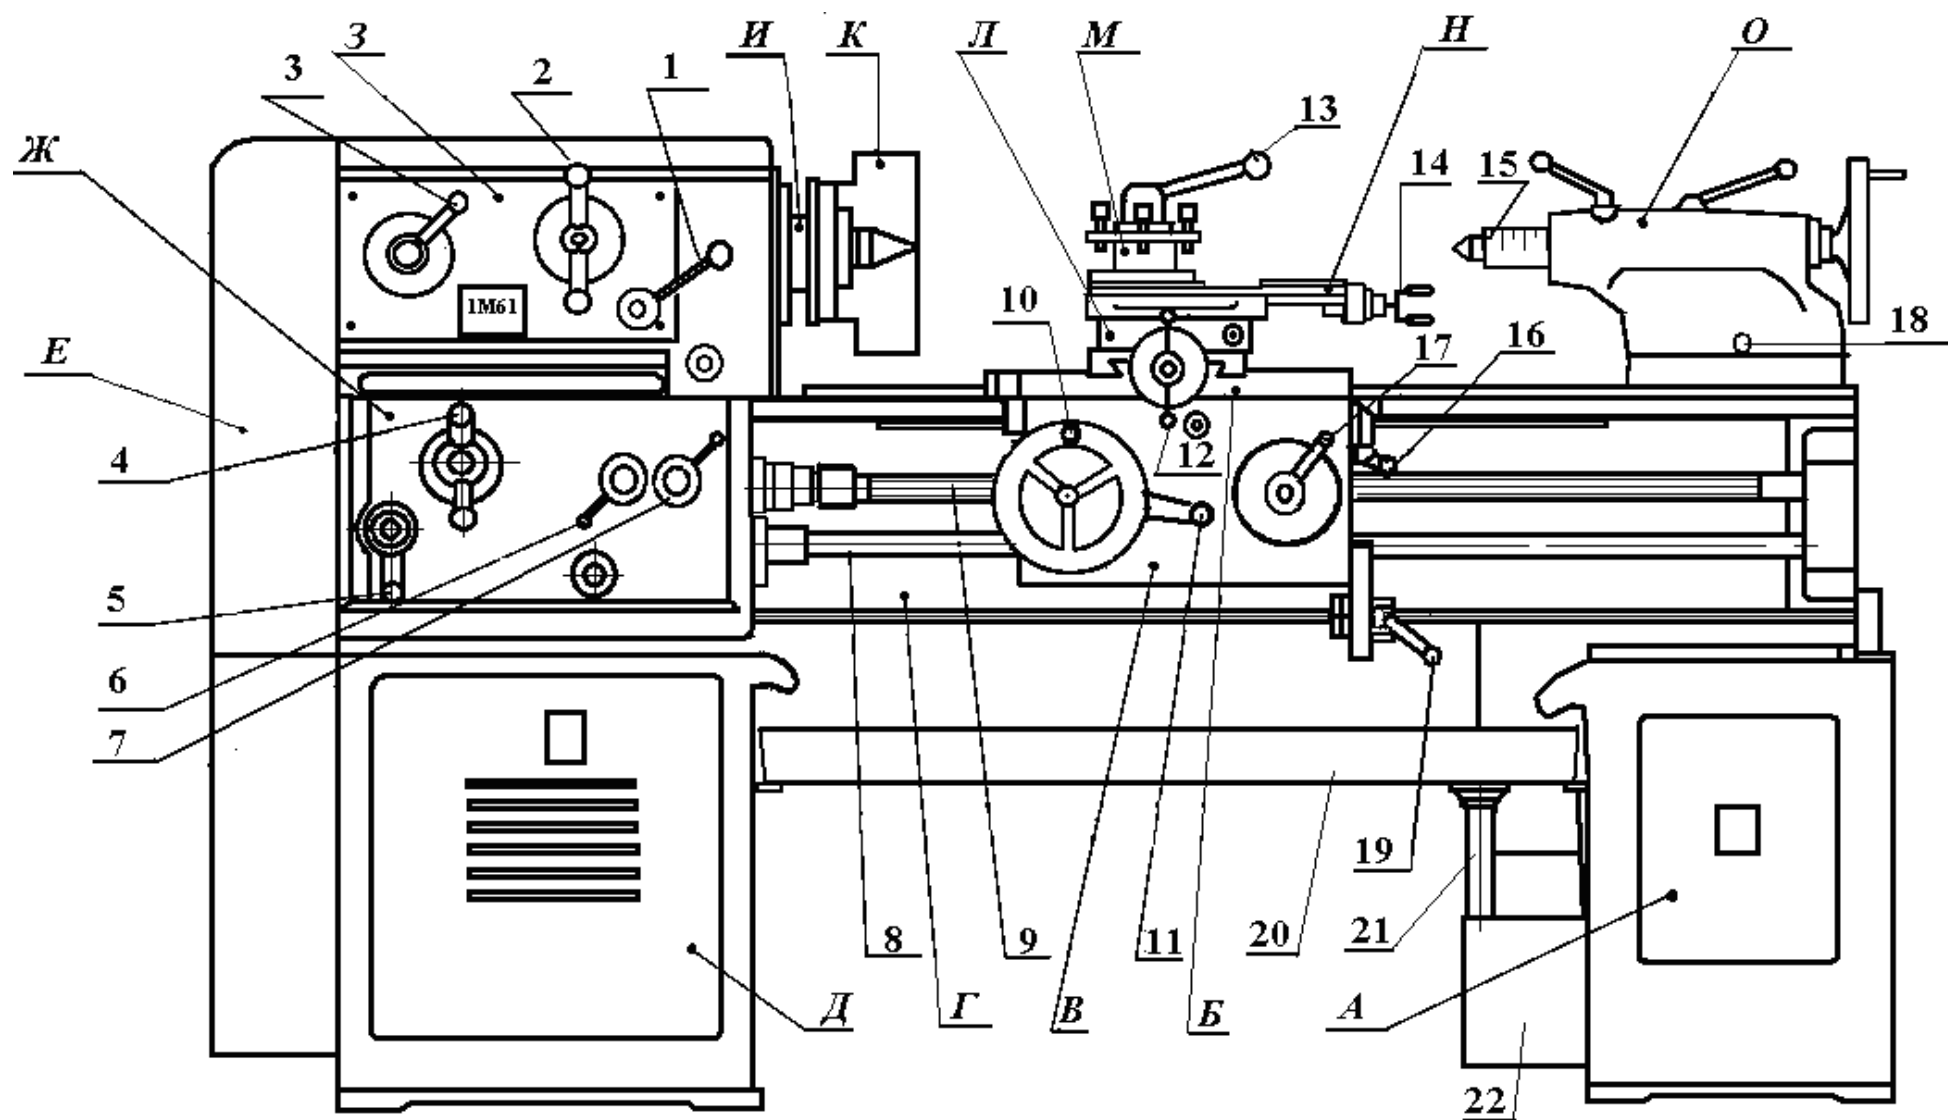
2. Общий вид токарно-винторезного станка 1М61
